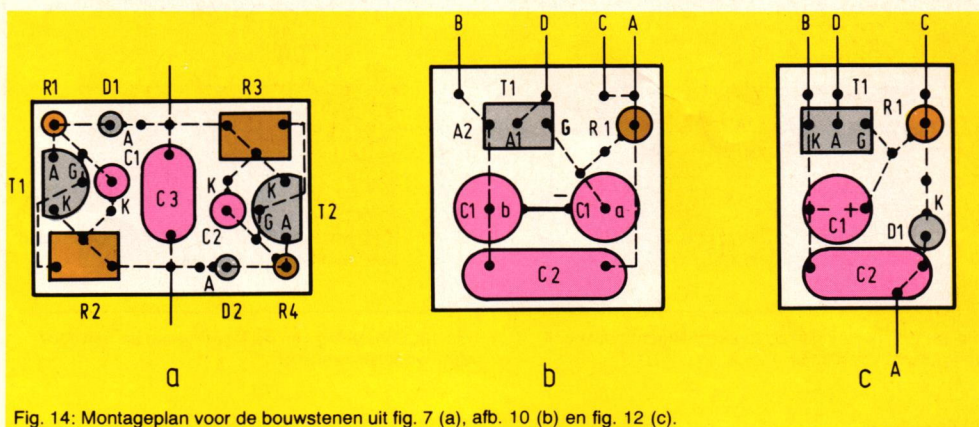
Montageplan voor de bouwstenen uit fig. 7 (a), afb. 10 (b) en fig. 12 (c).
